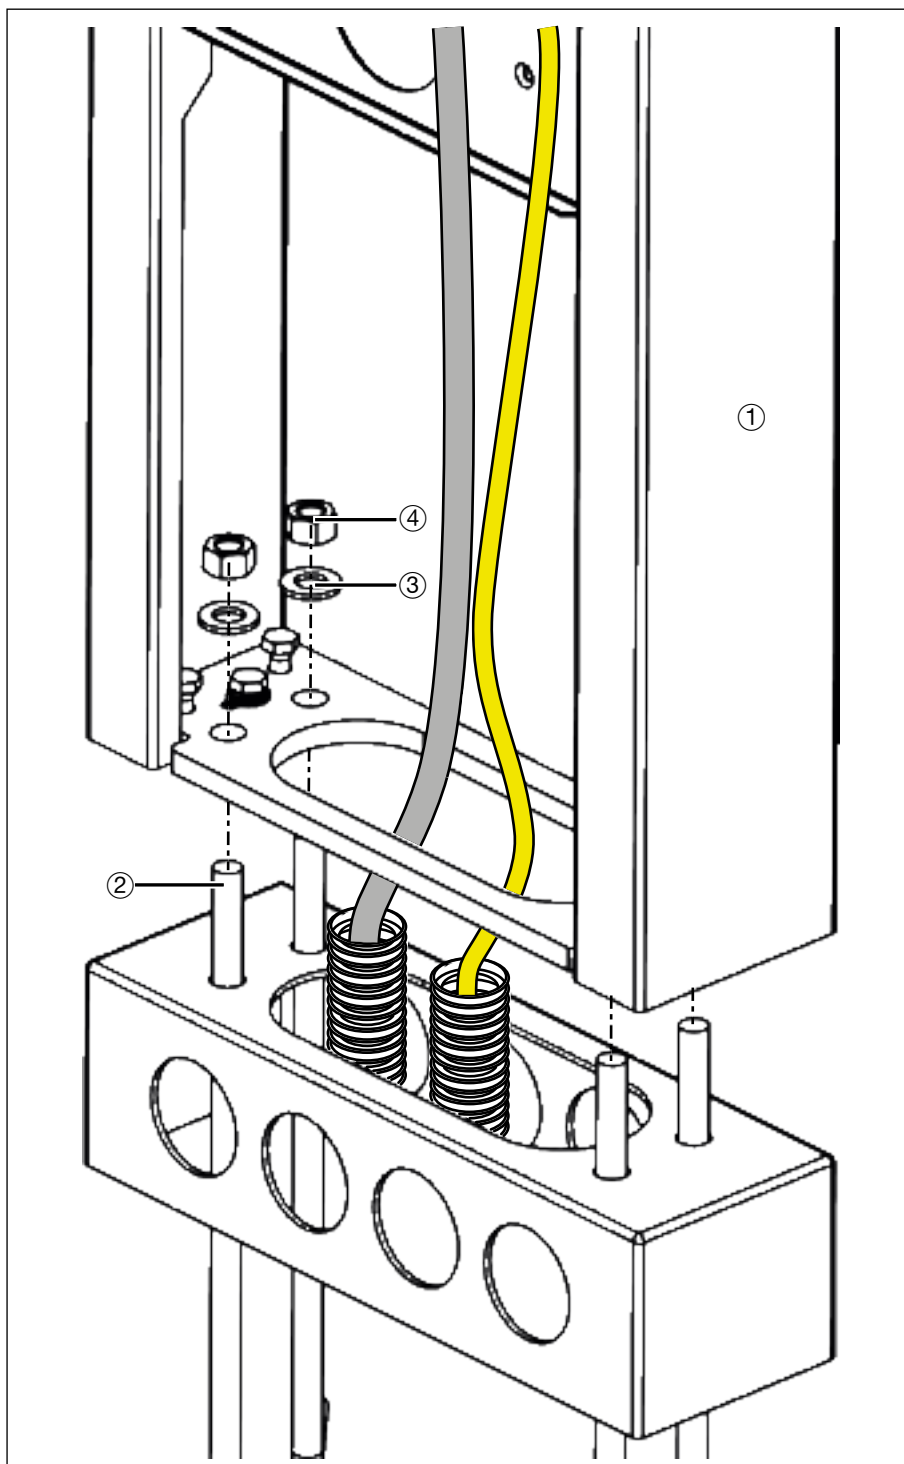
Monter le pied sur le socle de montage (vue de l'arrière)
